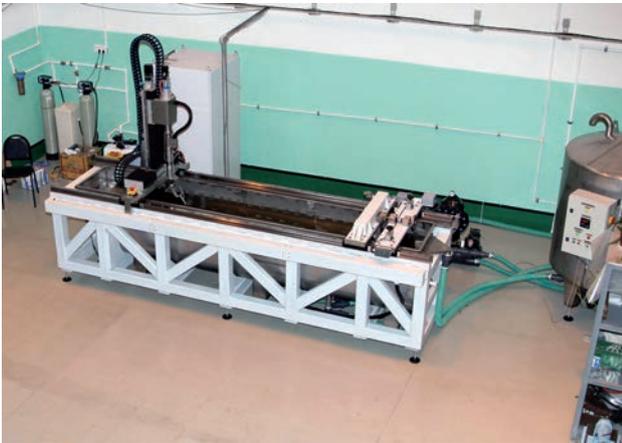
Установка АСНК-ВАЛ для контроля заготовок валов авиационных двигателей. АО «ПМЗ»
